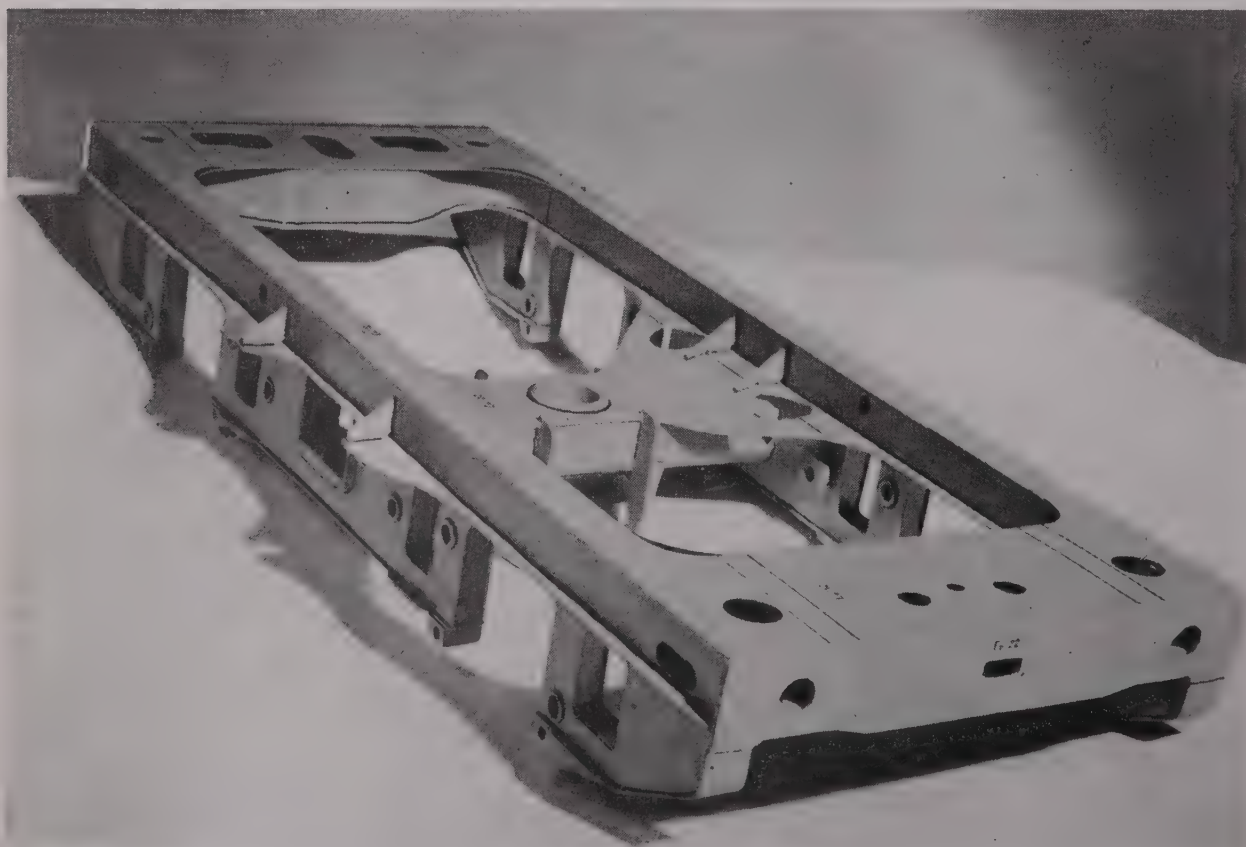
Locomotives B.B. 8 100 de la S. N. C. F. Châssis de bogie entièrement soudé.
